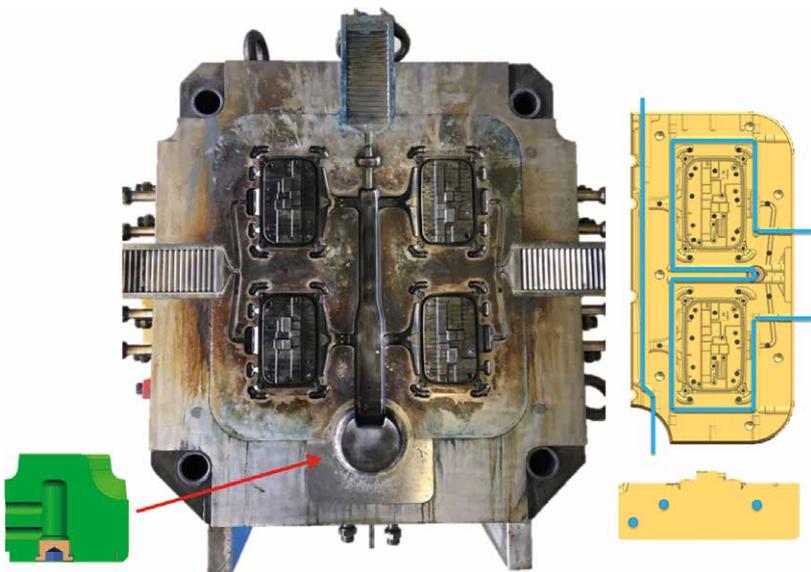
4-fach Serienwerkzeug für den Kühlkörper aus Aluminium-Druckguss. Die Werkzeugeinsätze und der Amboss verfügen über konventionelle Kühlkanäle und Stichkühlungen.
